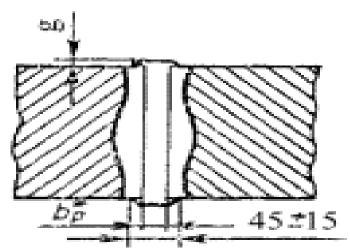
Требования геометрических размеров сварного шва для C1 по ГОСТ 15164
